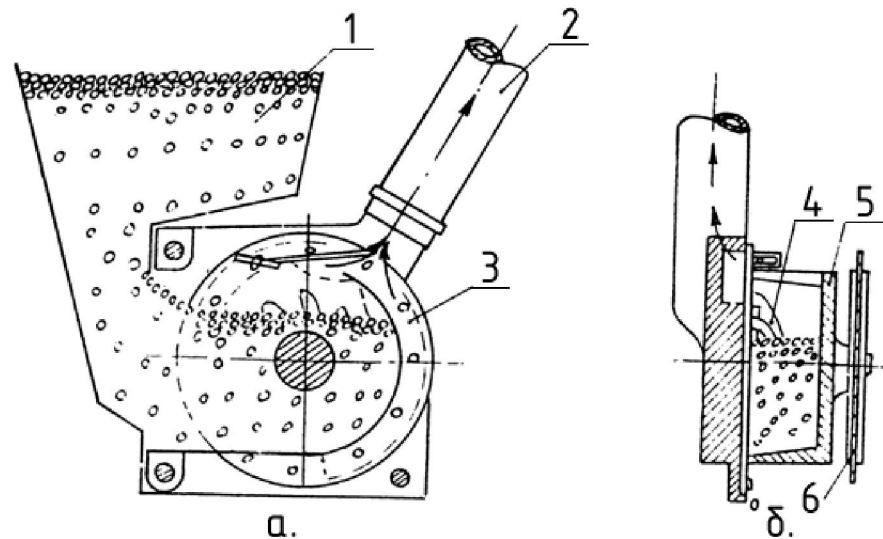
Схема дискового пневматичного висівального апарата з горизонтальною віссю обертання: *а* – вид збоку; *б* – вид попереду; 1- бункер для насіння; 2- воздуховод; 3- висівальний диск; 4- ворошитель насіння; 5- корпус; 6- приводна зірочка
